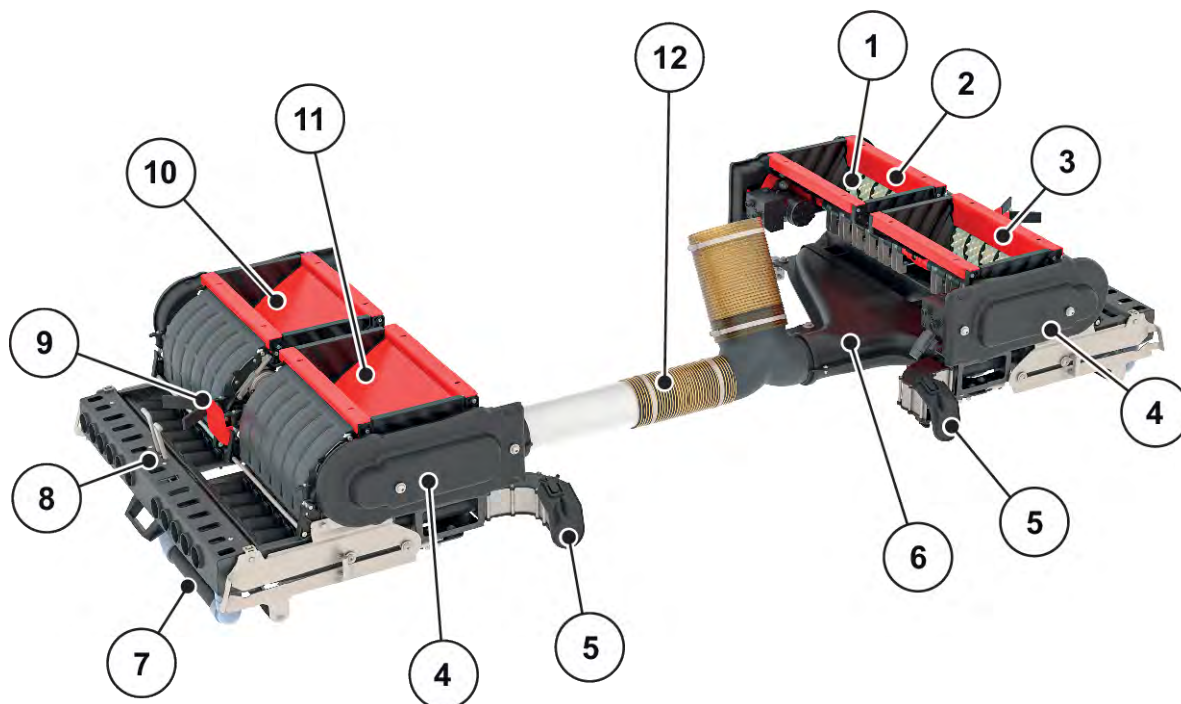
Maskinens komponentgrupper og funksjoner, bakside
